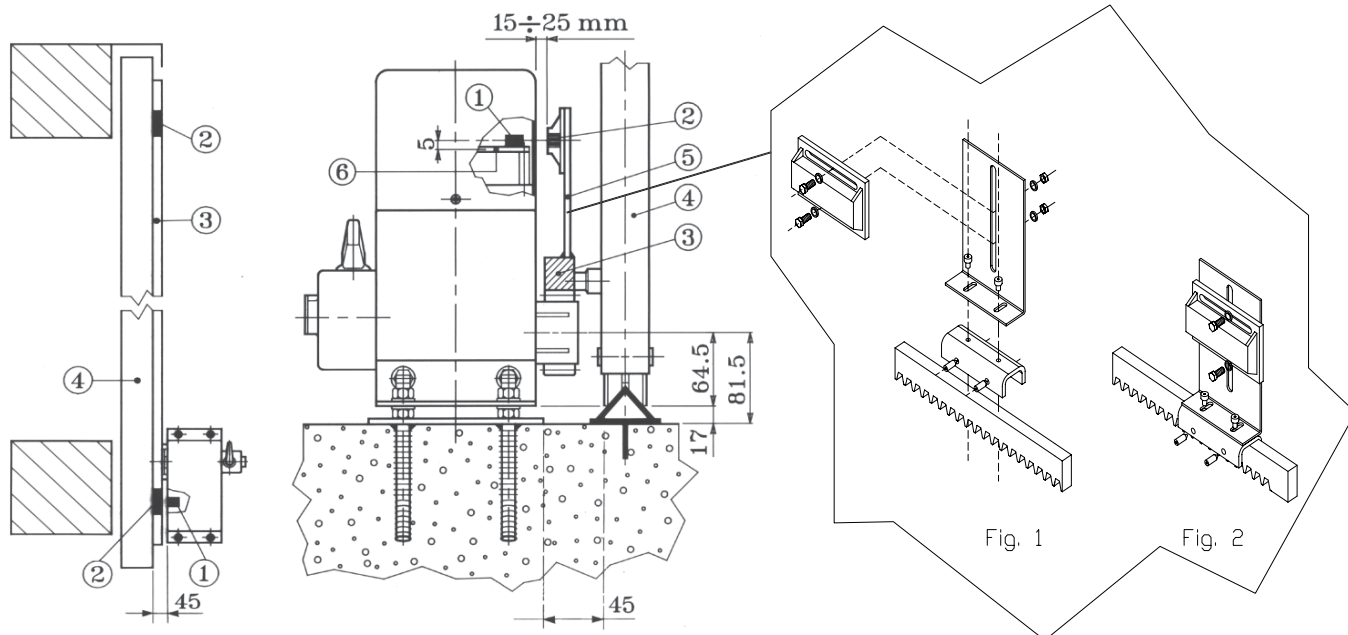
Jeu minimum entre l'engrenage et la crémaillère
